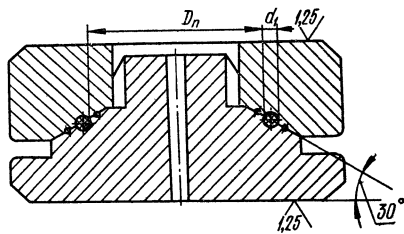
Пресс-форма для изготовления уплотнительных колец.
